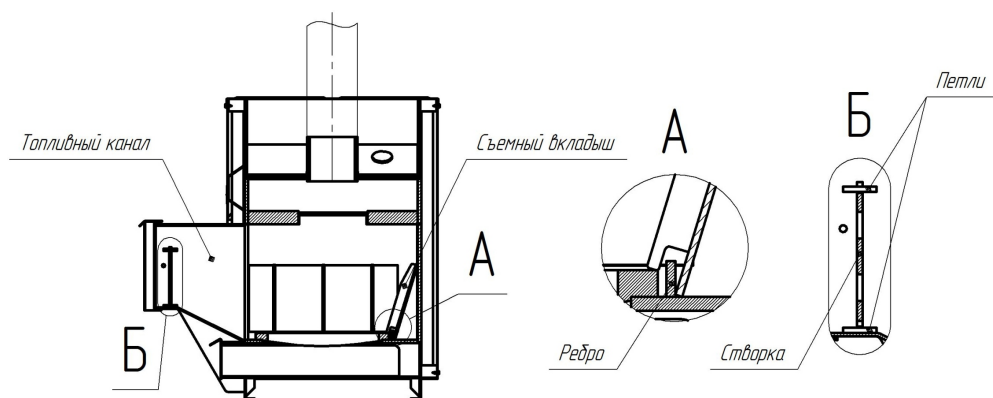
а - Установка боковых вкладышей под уголь в топку печи для бани
